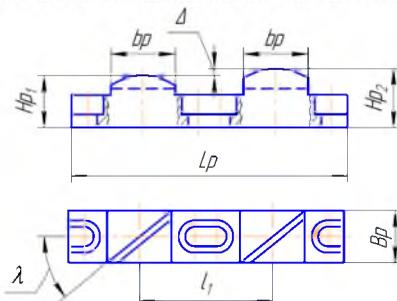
Конструкция резца-зуба развёртки со сдвоенными безвершинными зубьями с разными диаметрами
